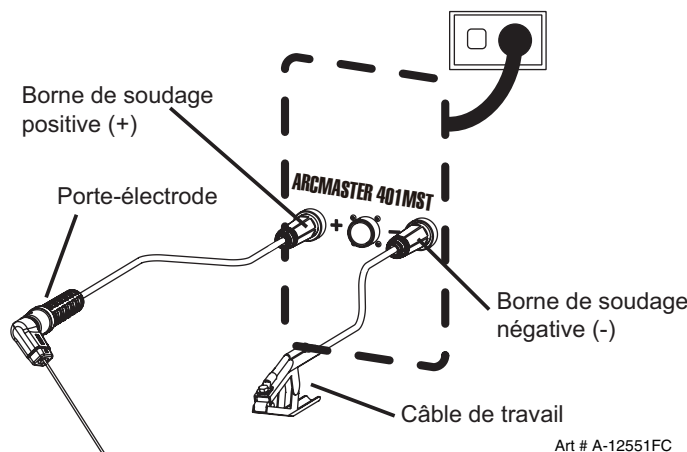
Configuration pour soudage à l'électrode enrobée (procédé SMAW)
